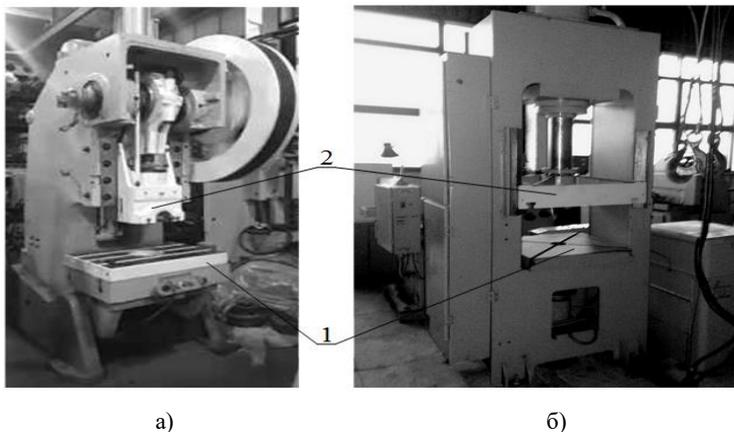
Прессы для листовой штамповки: а) кривошипный, б) гидравлический: 1 – стол прессы, 2 – ползун (поперечина) прессы
